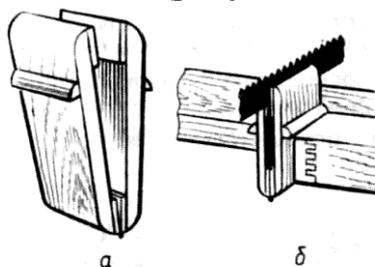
Инструмент для разводки и проверки развода зубьев пил
